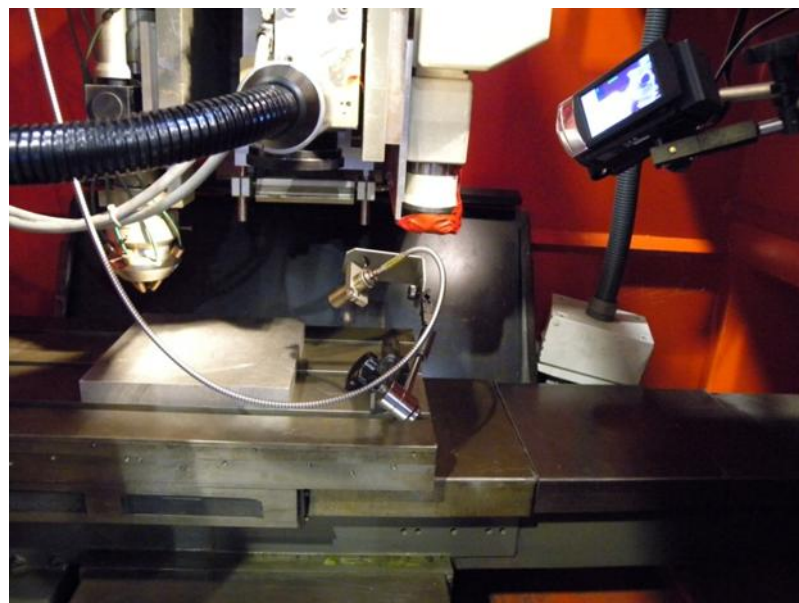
Загальний вигляд обладнання для лазерного термооброблення (а)
